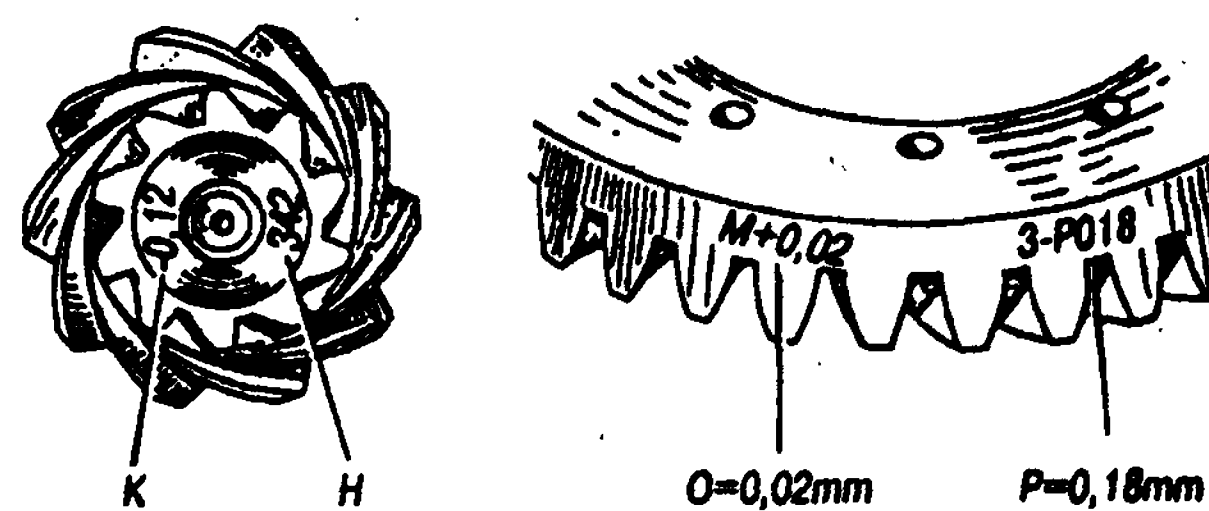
Маркировка шестерен главной передачи: Н - порядковый номер пары шестерен; К - отклонение высоты головки ведомой шестерни; О - отклонение монтажного размера ведомой шестерни; Р - боковой зазор в паре
